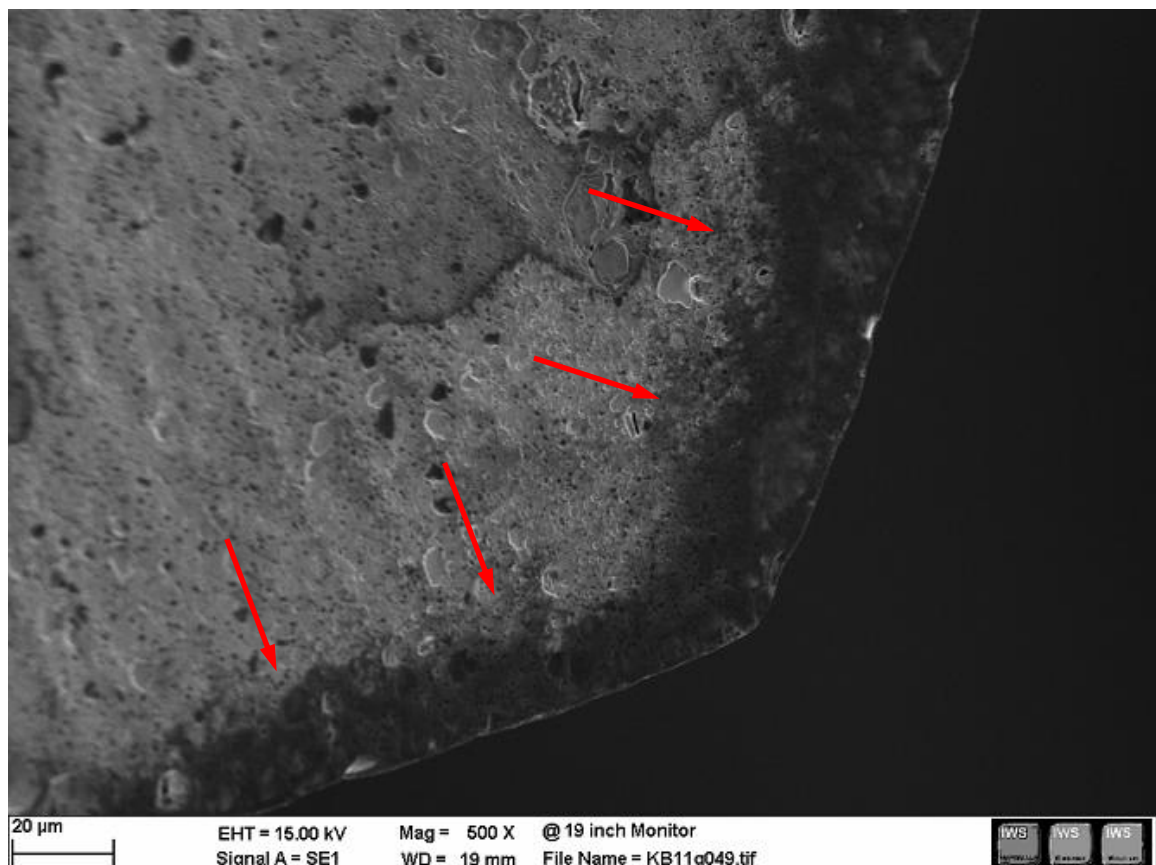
Detail X; Brasseler Standard 440B; 40 Bohr. FSW; REM (500 X)
